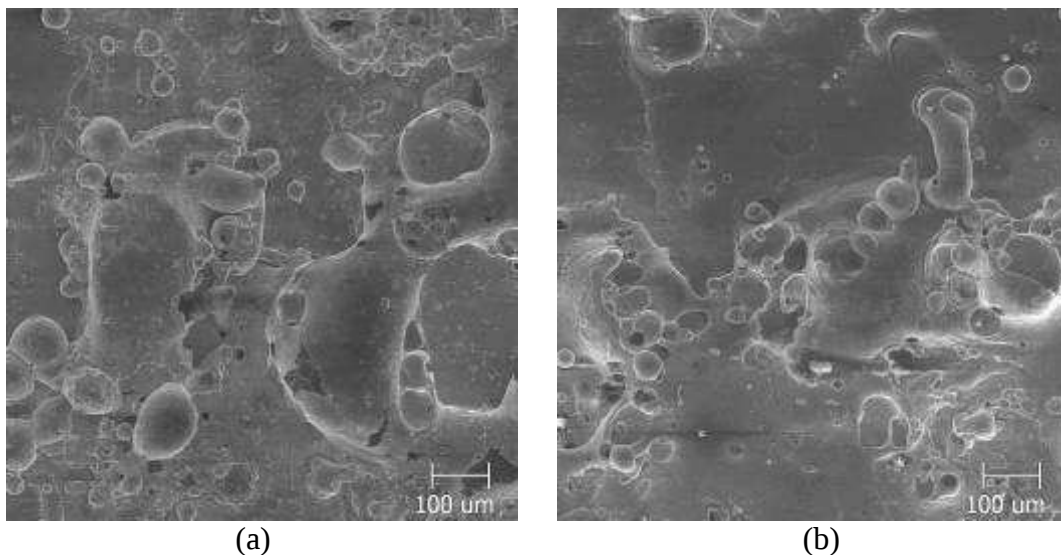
Imagens obtidas via MEV das superfícies usinadas por EDM com fluido mineral sintético utilizando ferramenta de: (a) cobre e (b) grafite.
